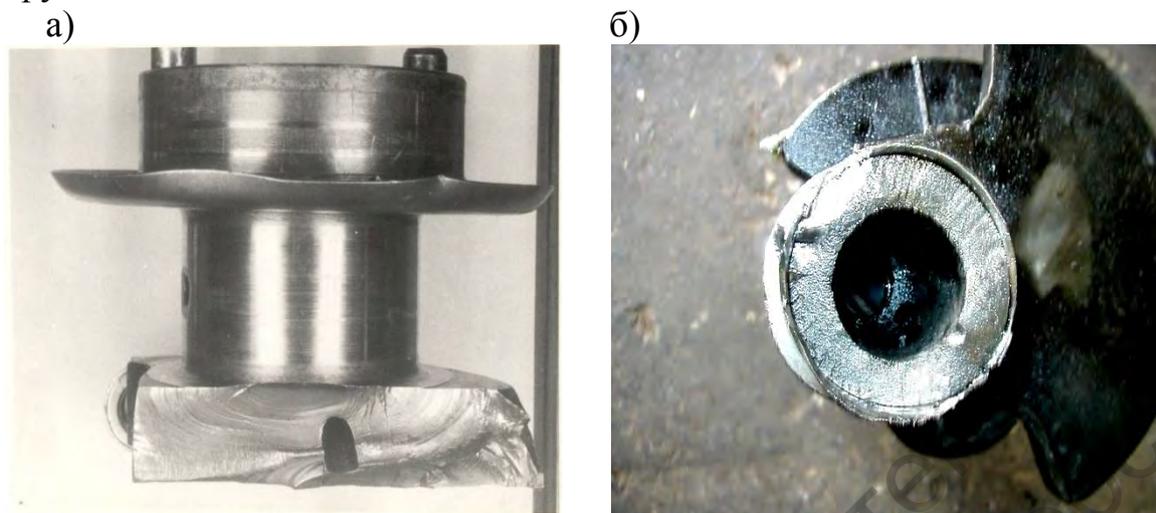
Макроусталостные линии на поверхностях излома щеки (а) и шейки (б) коленчатого вала, изготовленного из чугуна ВЧ50
